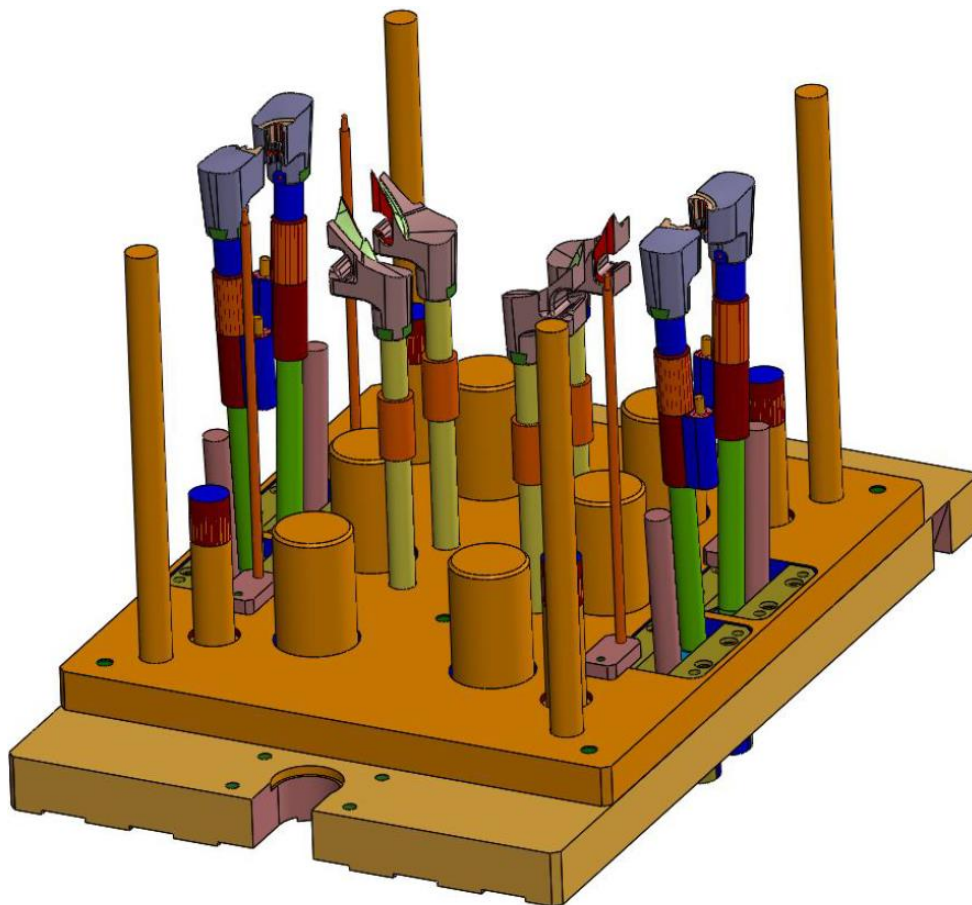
Vista Isométrica da placa de extração e seus componentes
